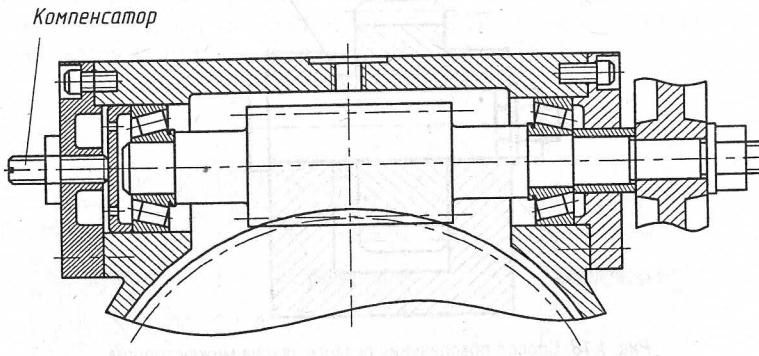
Способ регулирования величины осевого зазора в конических роликовых подшипниках с помощью винта
